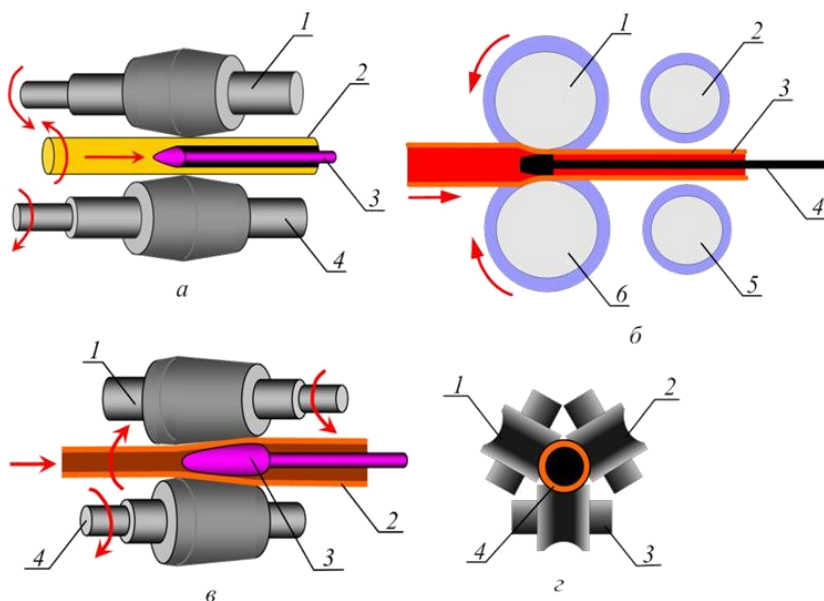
Схемы изготовления трубы на трубoproкатном агрегате:
